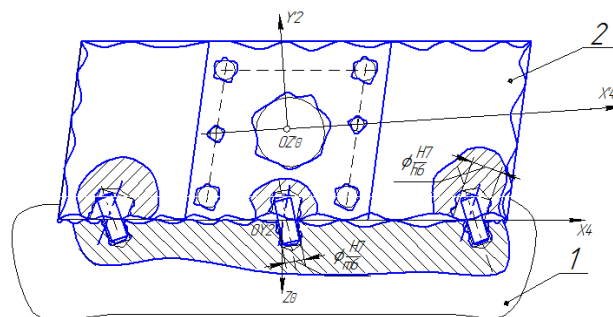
Геометрическая модель блока цилиндра в сборе с корпусом
